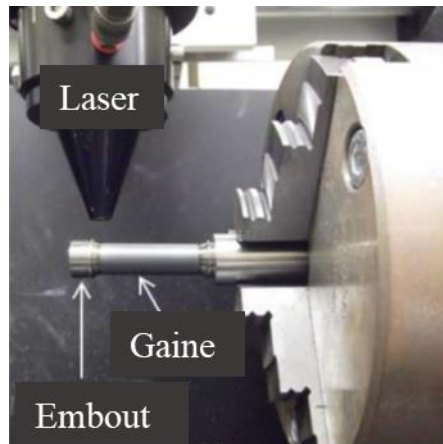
Vue de l'assemblage de l'éprouvette EDC avec traction
